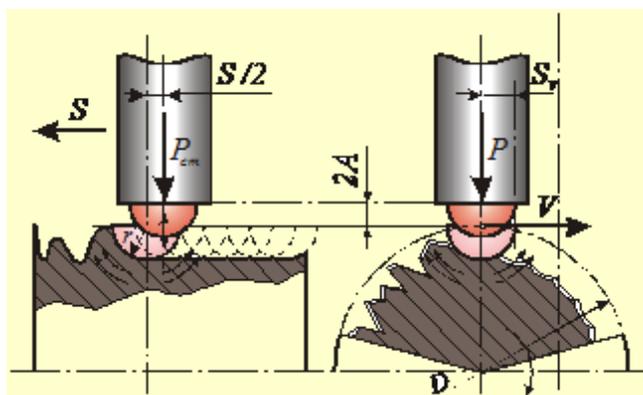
Схема поверхностного пластического деформирования при ультразвуковой упрочняющей обработке
